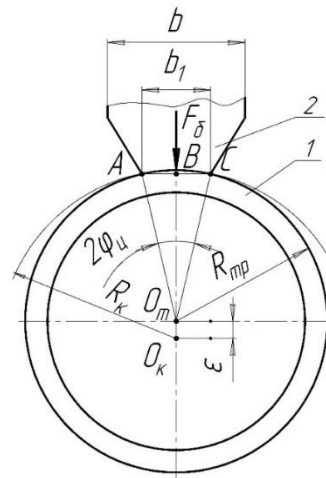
Розрахункова схема для визначення радіуса кулачка R_k , який створюється розточуванням: 1 – заготовка (труба); 2 – кулачок трикулачкового патрона.
